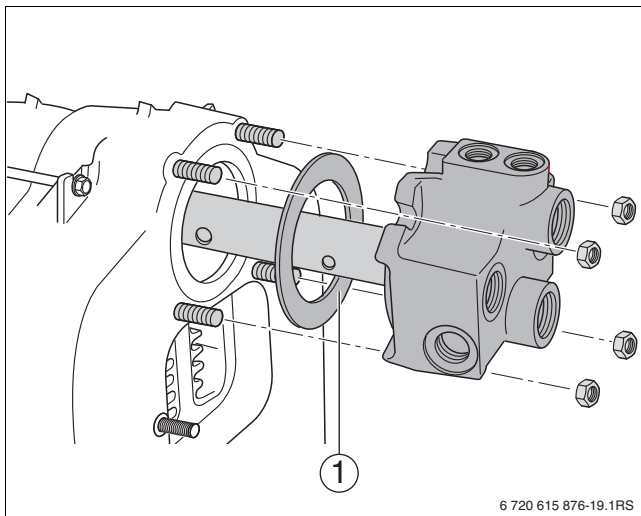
Montaje del tubo thermostream y del accesorio de conexión
